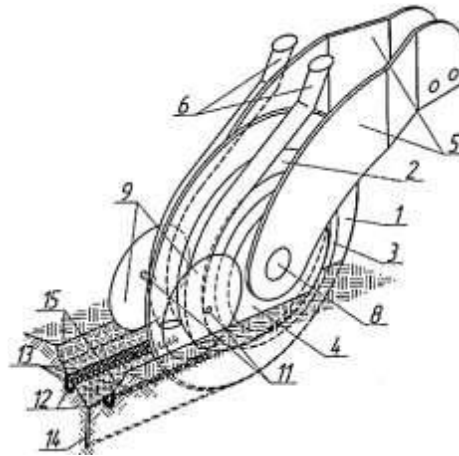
Технологічна схема роботи комбінованого однодискового сошника з двосторонніми ребордами та дисковими загортачами для вужькорядного посіву: 1 – плоский диск; 2 – внутрішня реборда; 3 – борозноутворювач; 4 – зовнішня реборда; 5 – корпус; 6 – насіннепровід; 8, 11 – осі; 9 – сферичні диски; 12 – ложа; 13 – насіння; 14 – щілина; 15 – борозенки.
